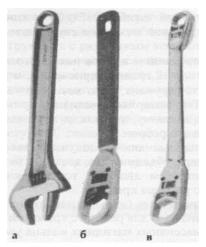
Разводные гаечные ключи: a — рожковый; δ — односторонний накидной; ϵ — двусторонний накидной
